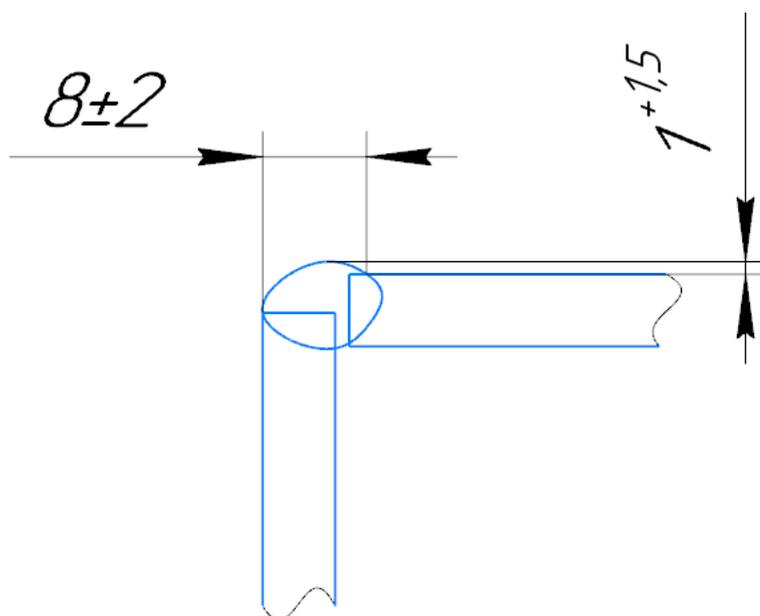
Размеры сварного шва У4 ГОСТ 14771-76
